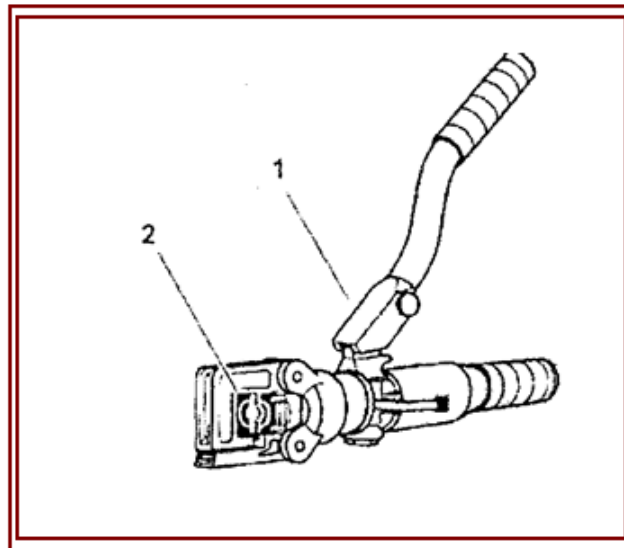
Ручной пресс для запрессовки соединительных втулок.
